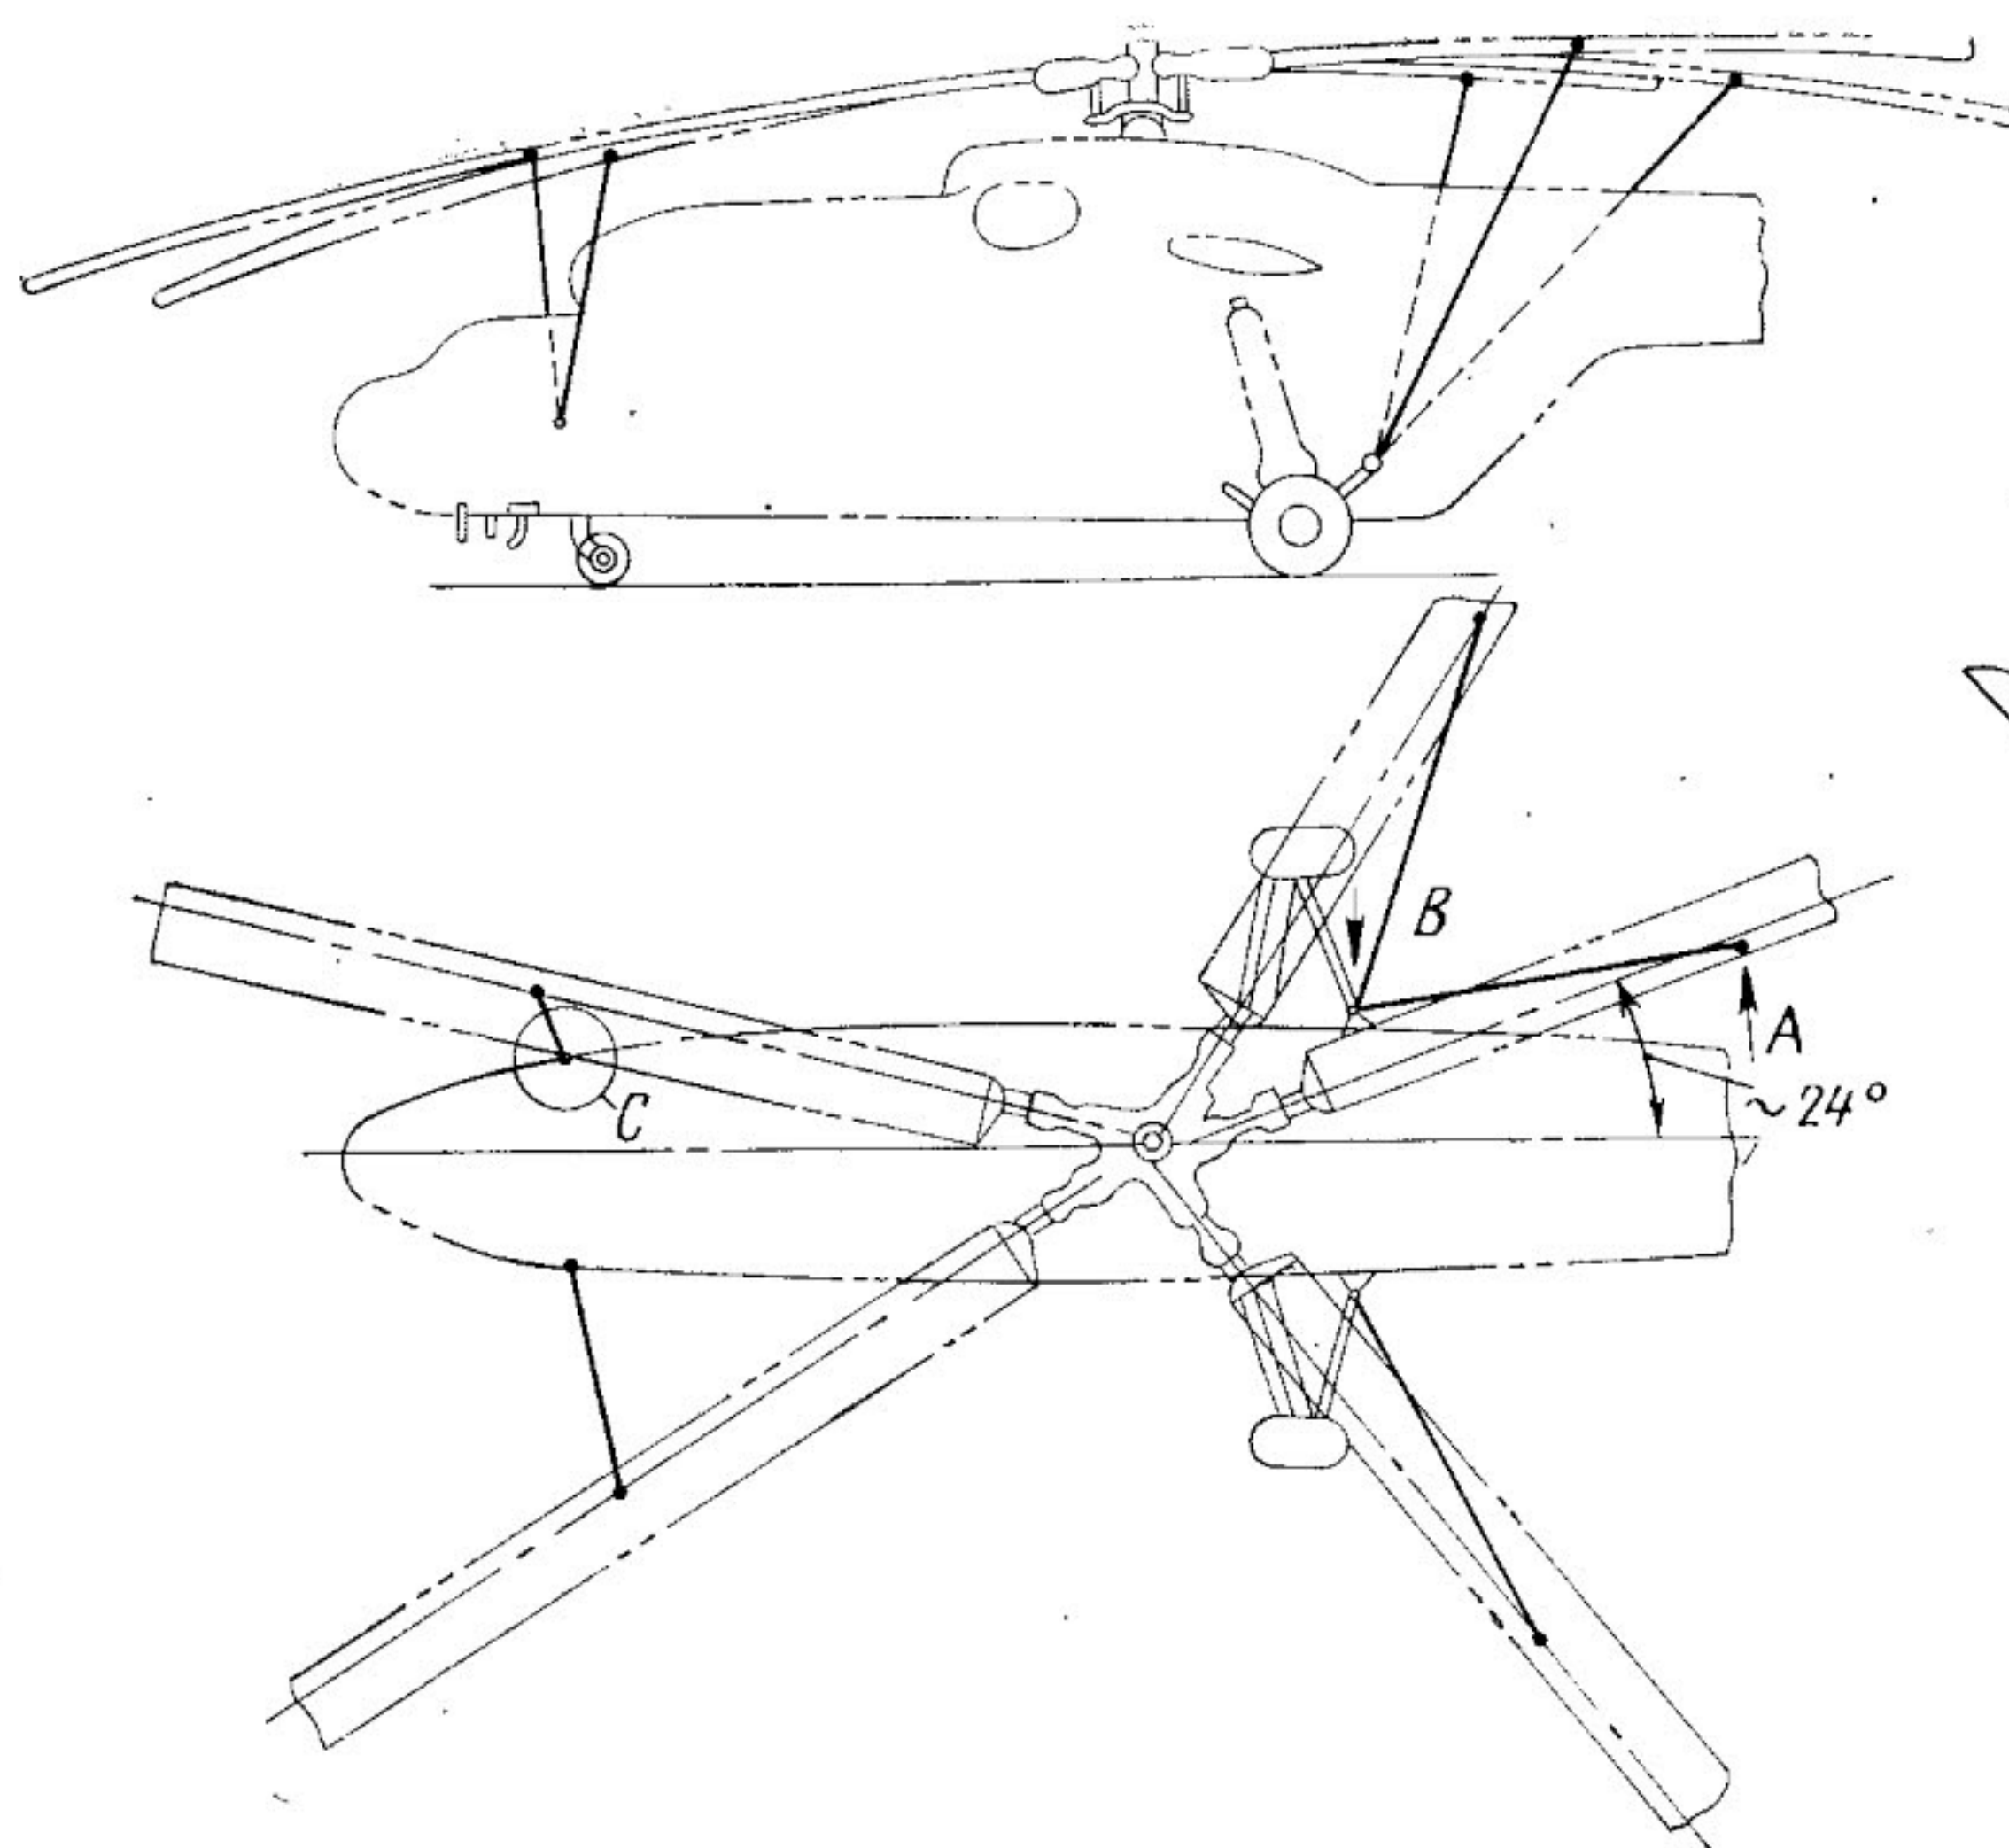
Приспособление для швартовки лопастей несущего винта:
